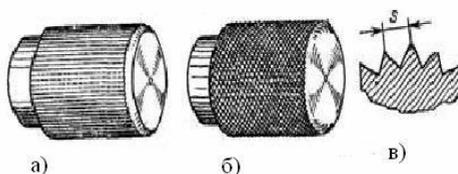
Схема накатки рифленых поверхностей: а – прямая; б – сетчатая; в – шаг накатки
